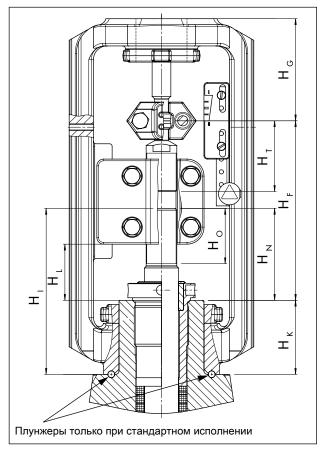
Чертеж с монтажными размерами для пневматических приводов Tun 3271 и Tun 3277
